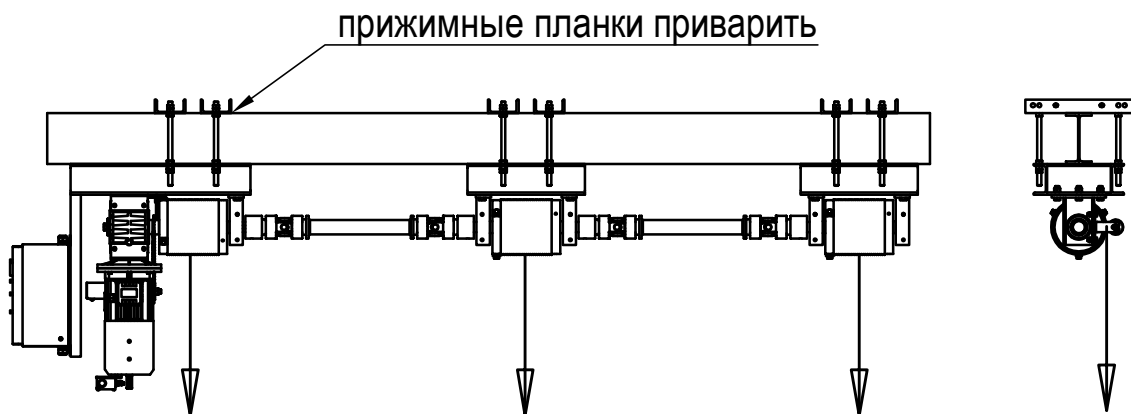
Возможный вариант крепления вальной лебедки прижимными планками к поперечным двутаврам
